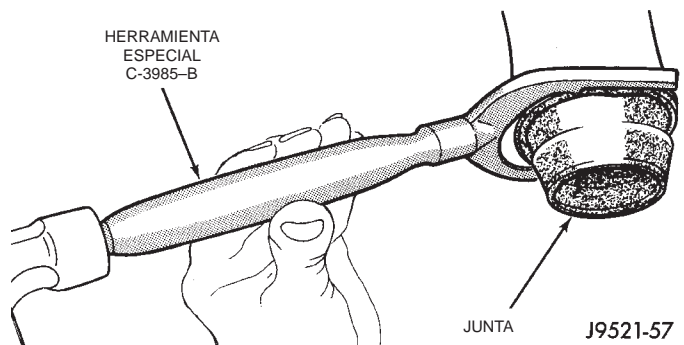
Desmontaje de la junta del estribo del retenedor de cojinete trasero
